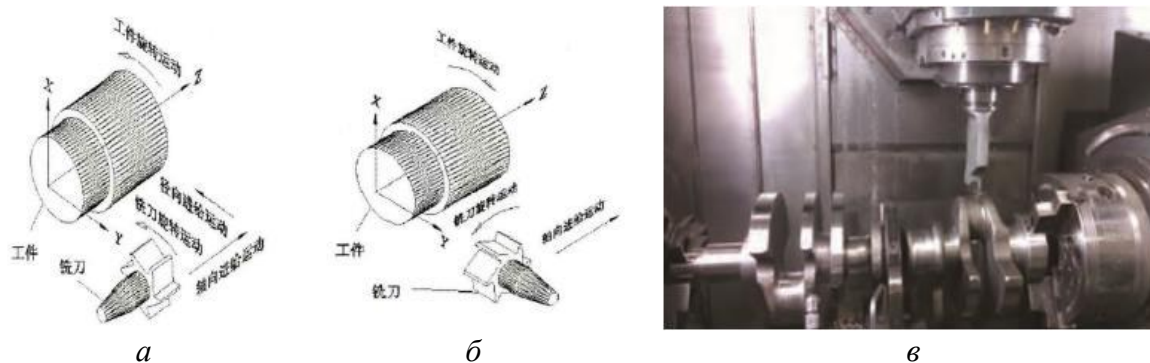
Обробка колінчастого вала периферією фрези (а), її торцем (б) та різцем (в) [18]
